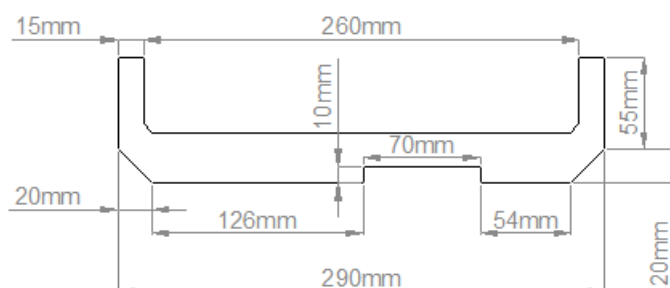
Desenho e dimensões dos apoios do computador portátil.
